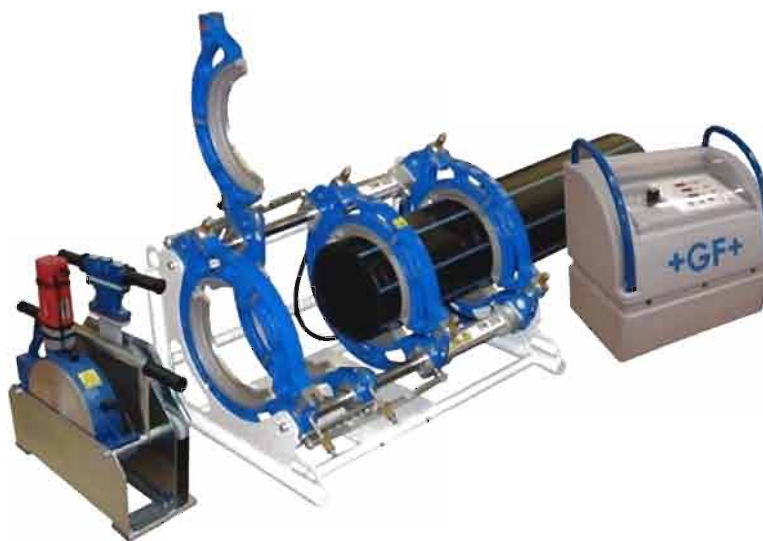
Оборудование для стыковой сварки труб фирмы GF (Georg Fisher), Швейцария
